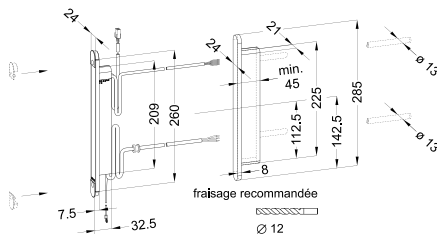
Dimensions de fraisage de transformateur pour dormant muni d'embout
